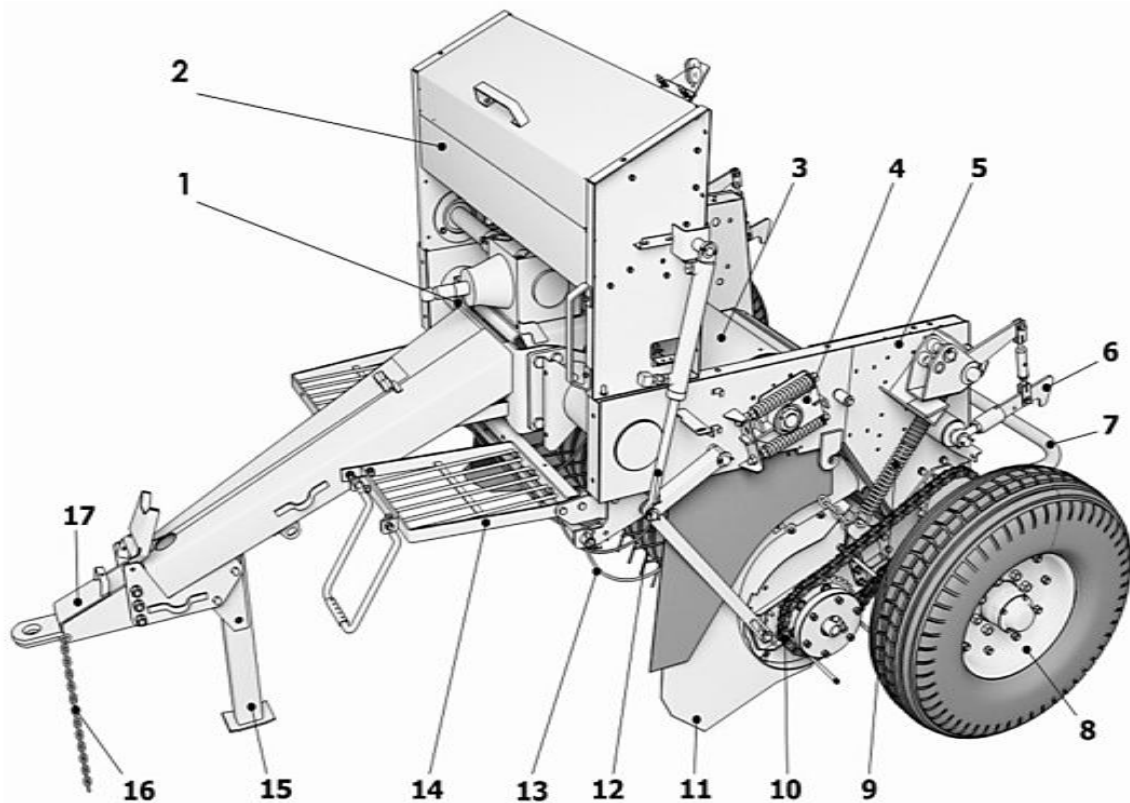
Шасси пресс-подборщика ППР-120: 1 – редуктор центральный; 2 – ящик-кассетница; 3 – подвижный нажимной валец; 4 – механизм регулировки плотности прессования; 5 – рама; 6 – подпружиненный крюк; 7 – скатная горка; 8 – опорное колесо; 9 – пружина вывешивания; 10 – цепь привода подборщика; 11 – подборщик; 12 – гидроцилиндр подъема подборщика; 13 – нормализатор; 14 – технологическая площадка; 15 – стояночная опора; 16 – цепь страховочная; 17 – прицепная скоба
